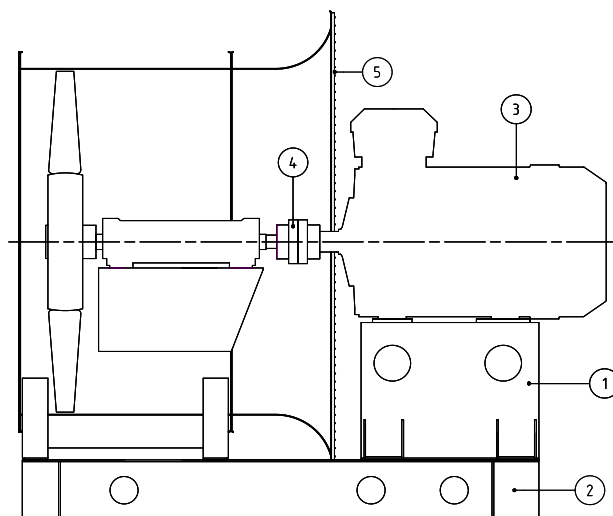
Zusammenbau des Axialventilators in Ausführung 8
